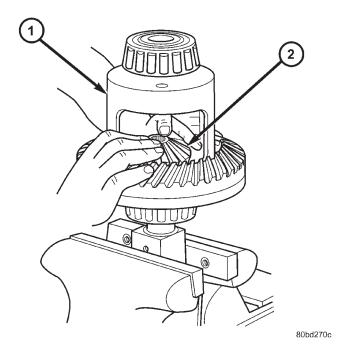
CONJUNTO DE EMBRAGUES Y ENGRANAJE LATERAL INFERIOR
